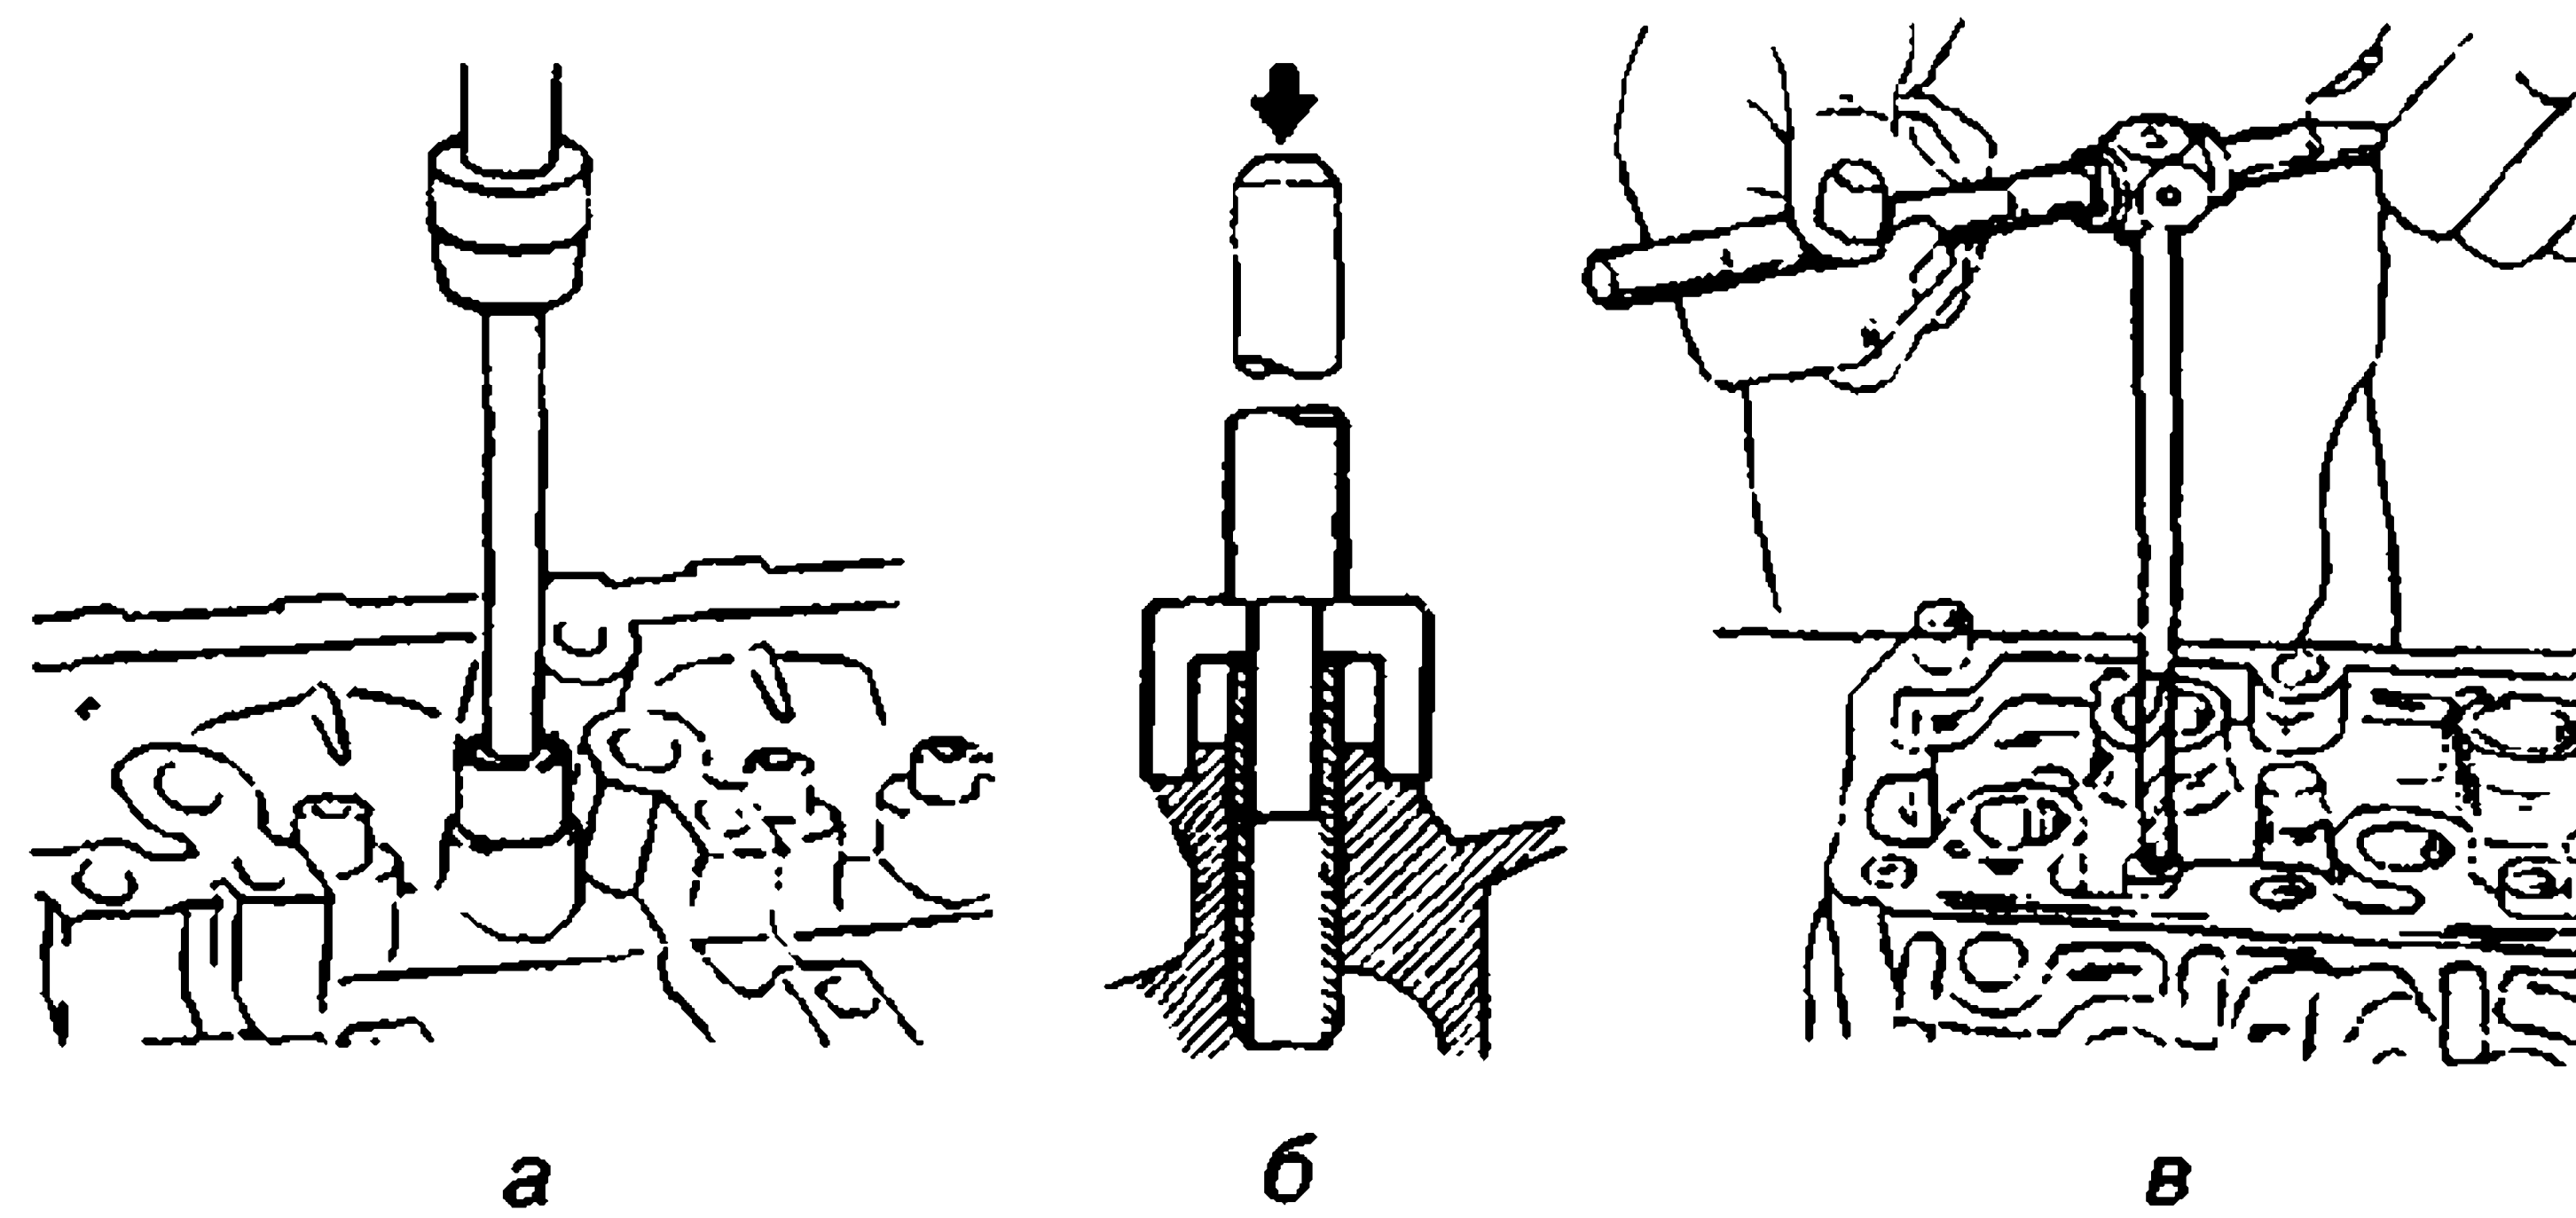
Запрессовка (а и б) и развертка (в) втулки клапана
